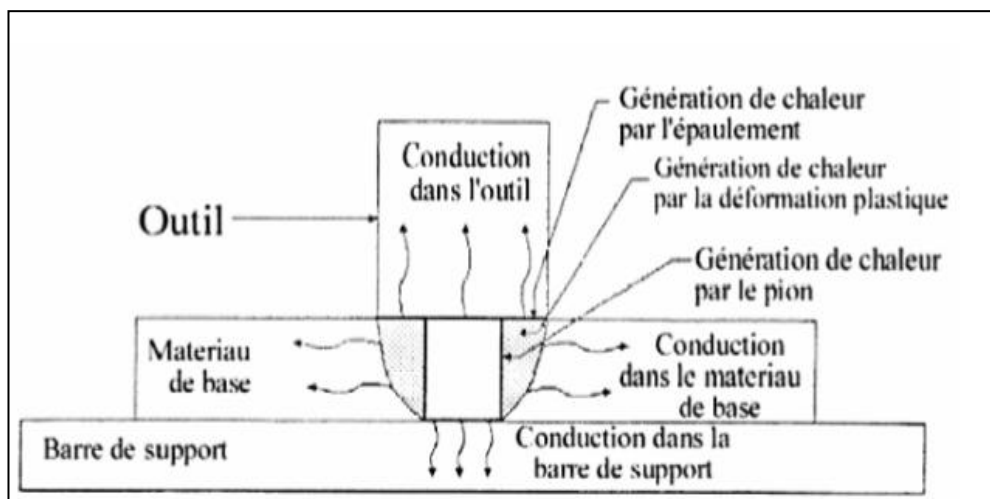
Transferts thermiques par conduction au cours du soudage FSW. [35]
